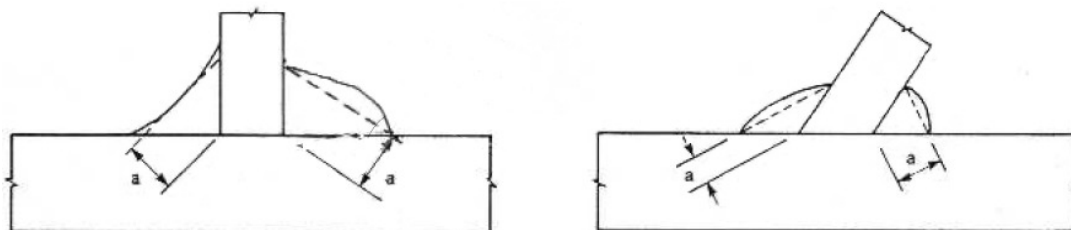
Espesor de garganta de las soldaduras en ángulo.
